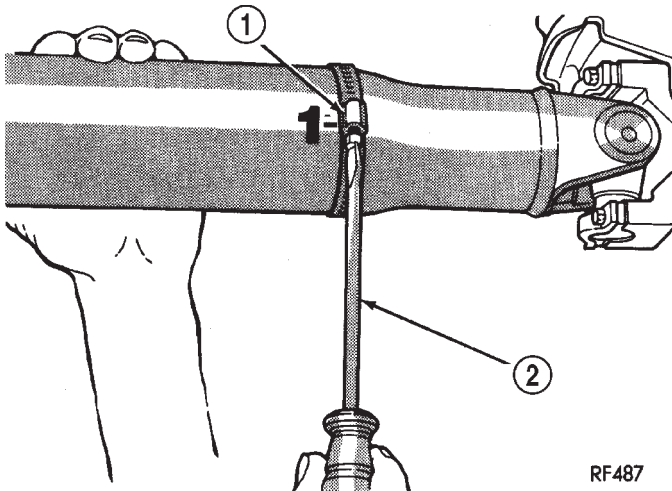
TORNILLO DE ABRAZADERA EN LA POSICIÓN 1
